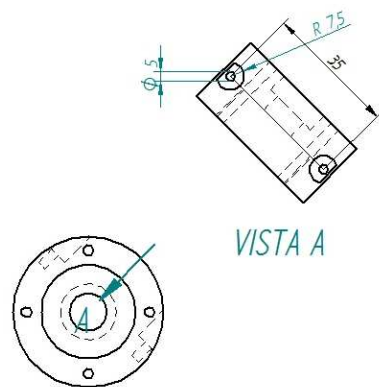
Vista detalle del plano de la pieza e imagen del detalle de la pieza acabada
